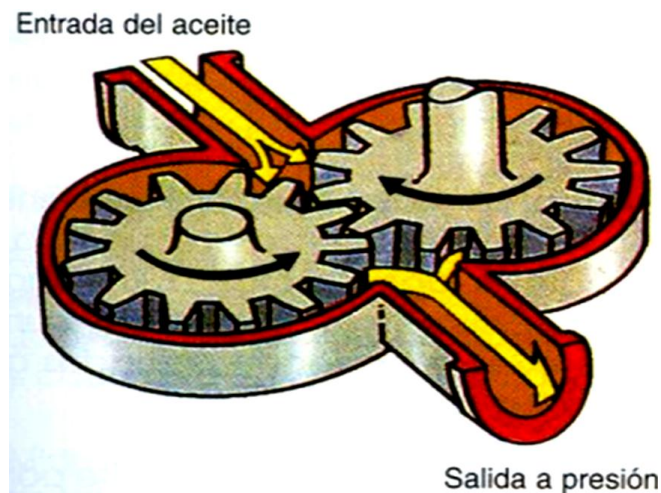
Bomba de engranajes. (Referencia 21).
